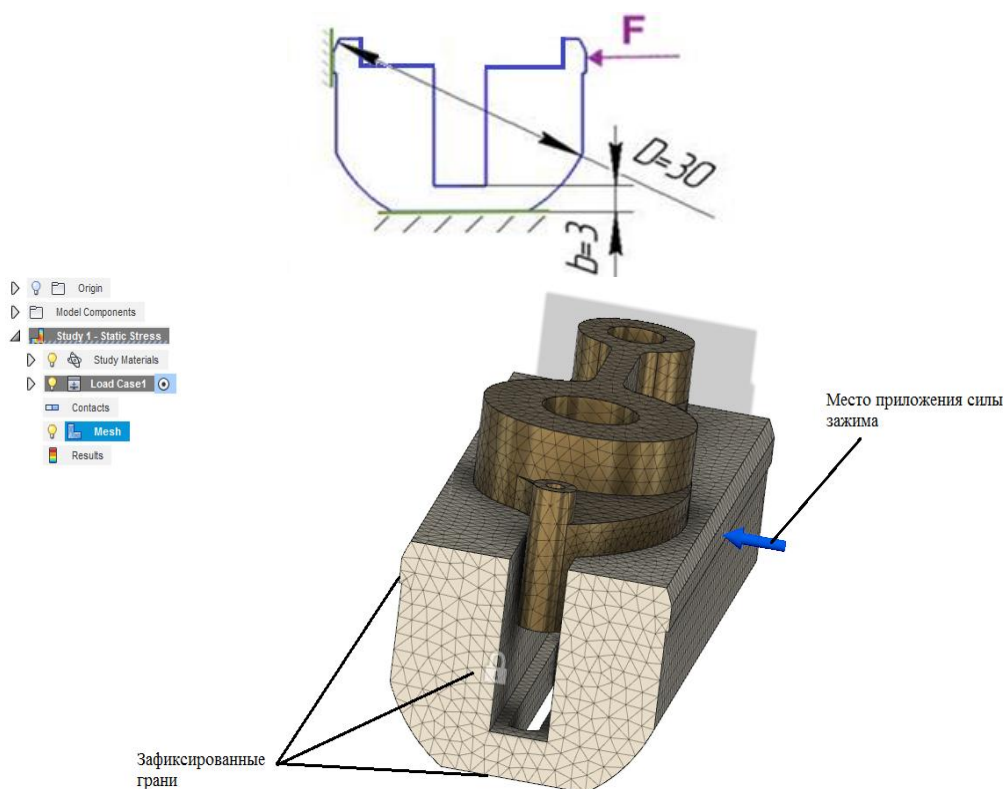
Схема расположения опорных поверхностей и прикладываемых нагрузок
